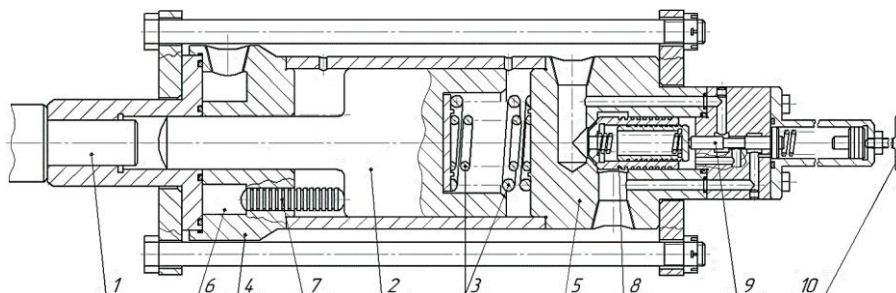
Конструктивна схема віброударного пристрою для руйнування гірських порід
